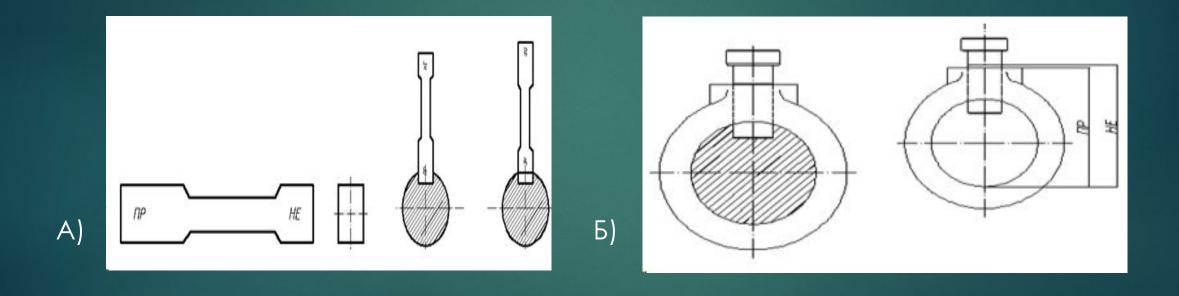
Контрольные калибры (а-калибр пластина; б- калибр кольцо)
